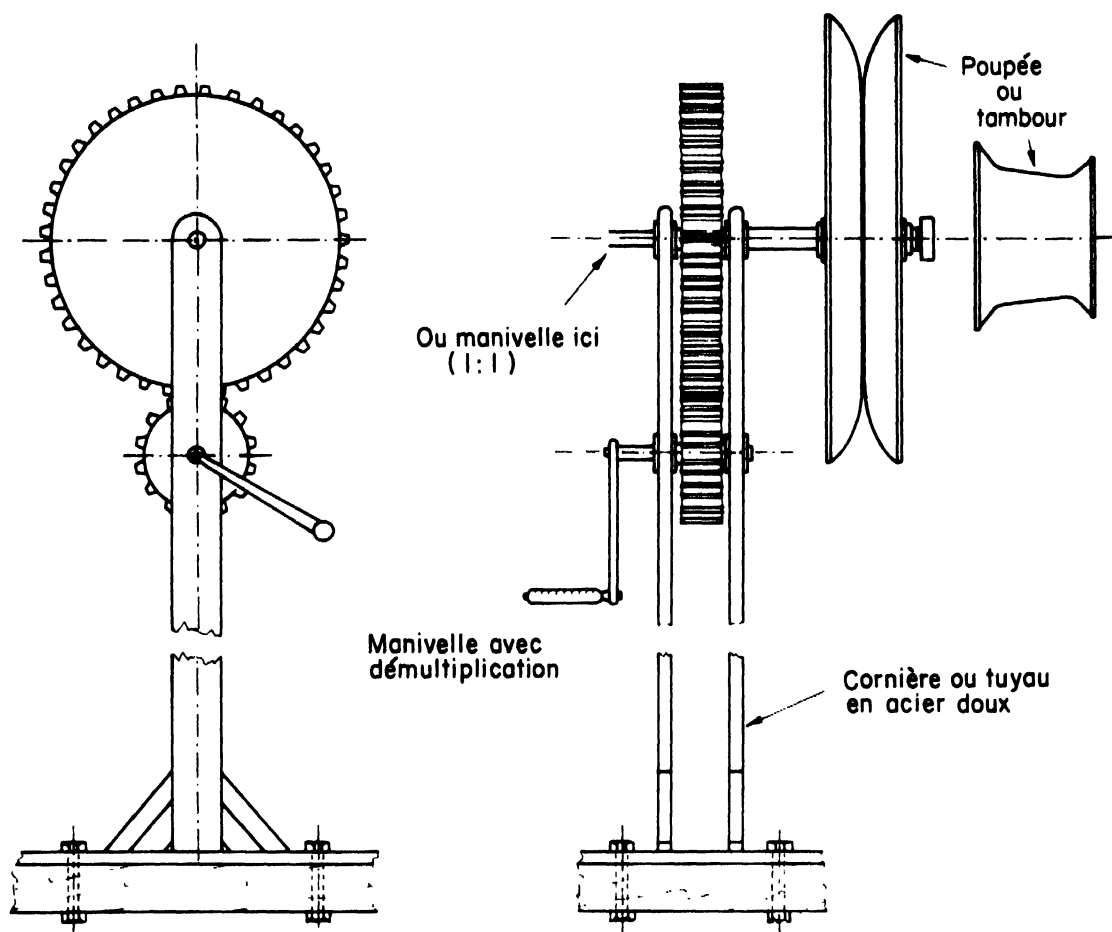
ENGIN DE LEVAGE A MAIN A ENGRENAGE
